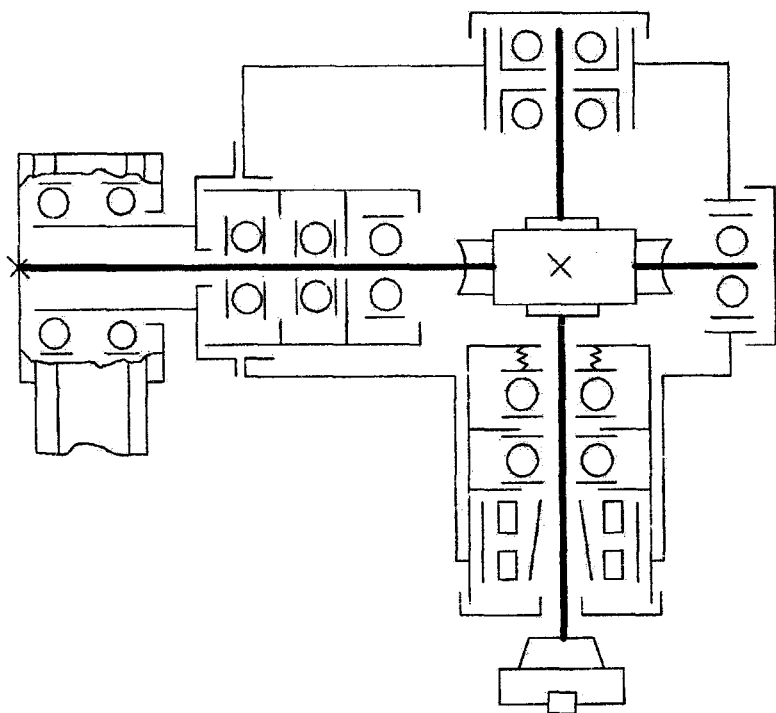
Кинематическая схема вертикальной фрезерной бабки агрегатного станка
